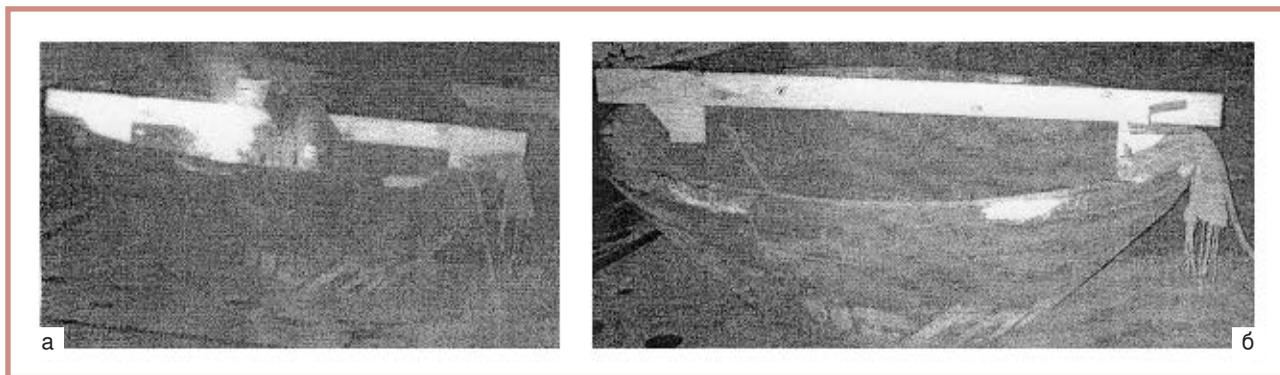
Восстановление чертежных размеров броневых плит после плазменно-механической обработки: а — рабочий момент ремонтной сварки; б — шаблон для регулирования в процессе сварки временных и остаточных сварочных деформаций
